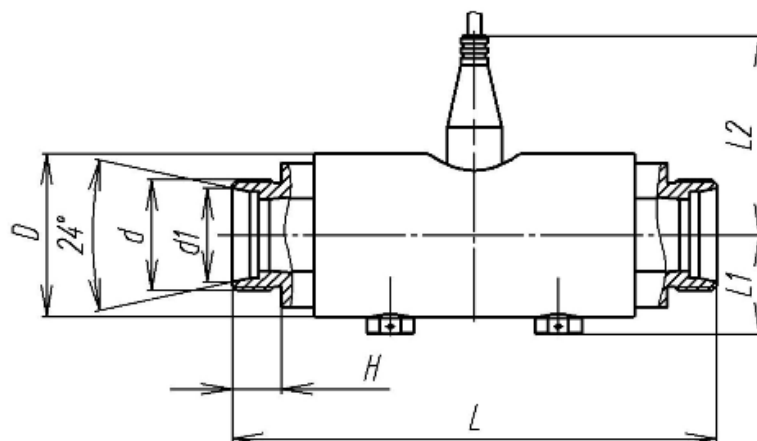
Габаритные и присоединительные размеры расходомеров-счётчиков РВШ-ТА-010-160-×-×× и РВШ-ТА-020-160-×-×× с резьбовым присоединением
